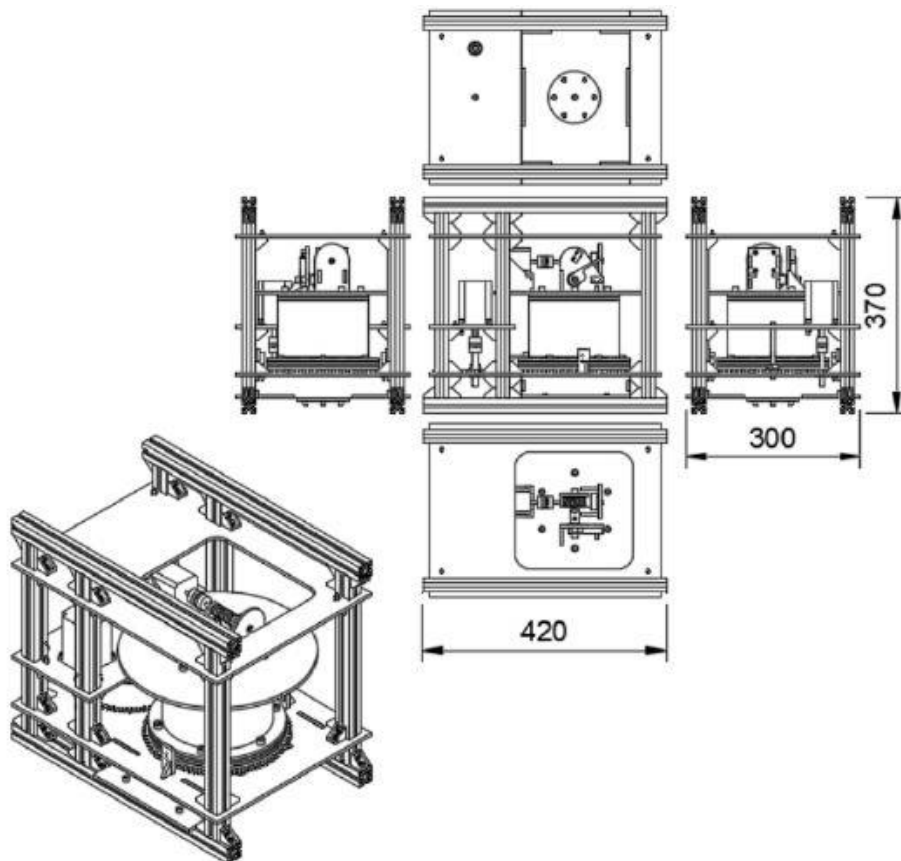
Ensamblaje final del prototipo del conjunto balanza + soporte.
